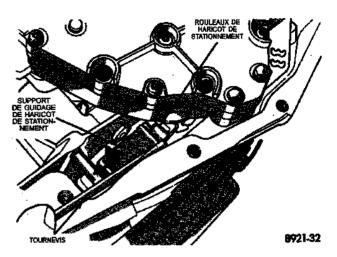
Pousser les rouleaux de la tige de stationnement depuis le support de guidage
